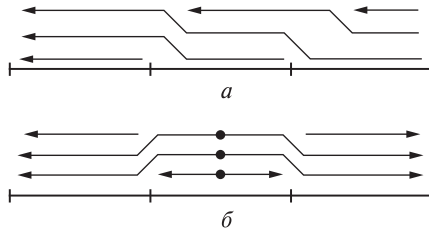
Последовательность выполнения многослойных швов при ручной и полуавтоматической сварке:
